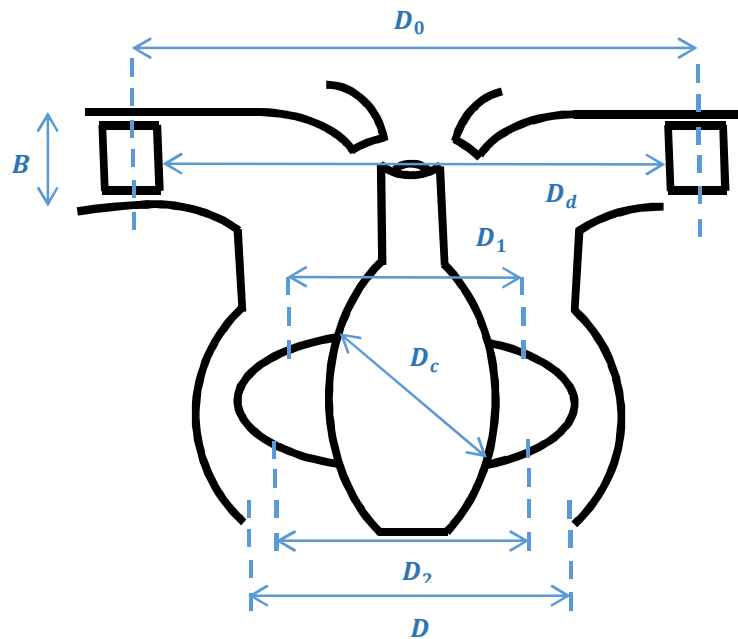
Dimensiones principales de una turbina Kaplán. Fuente: Elaboración propia.
